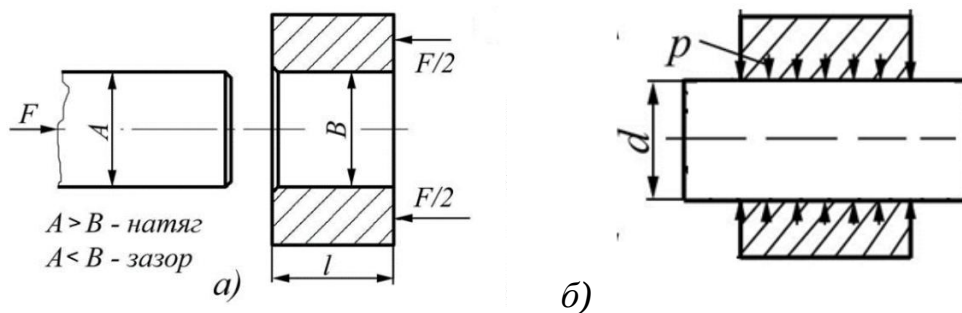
Соединение с натягом: а) до запрессовки; б) после запрессовки
